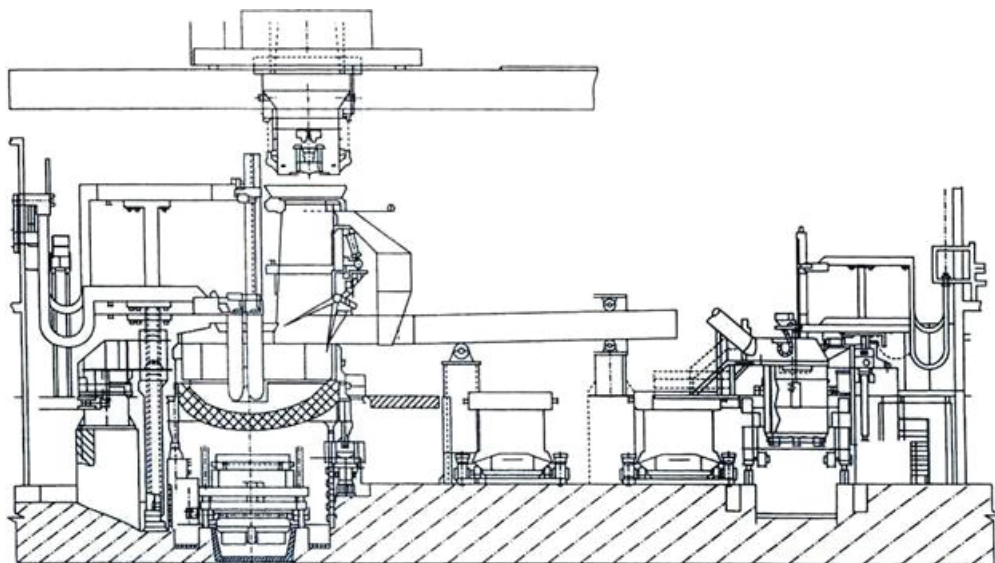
Разрез плавильного цеха на заводе фирмы Stahl Gerlafingen (Швейцария)
